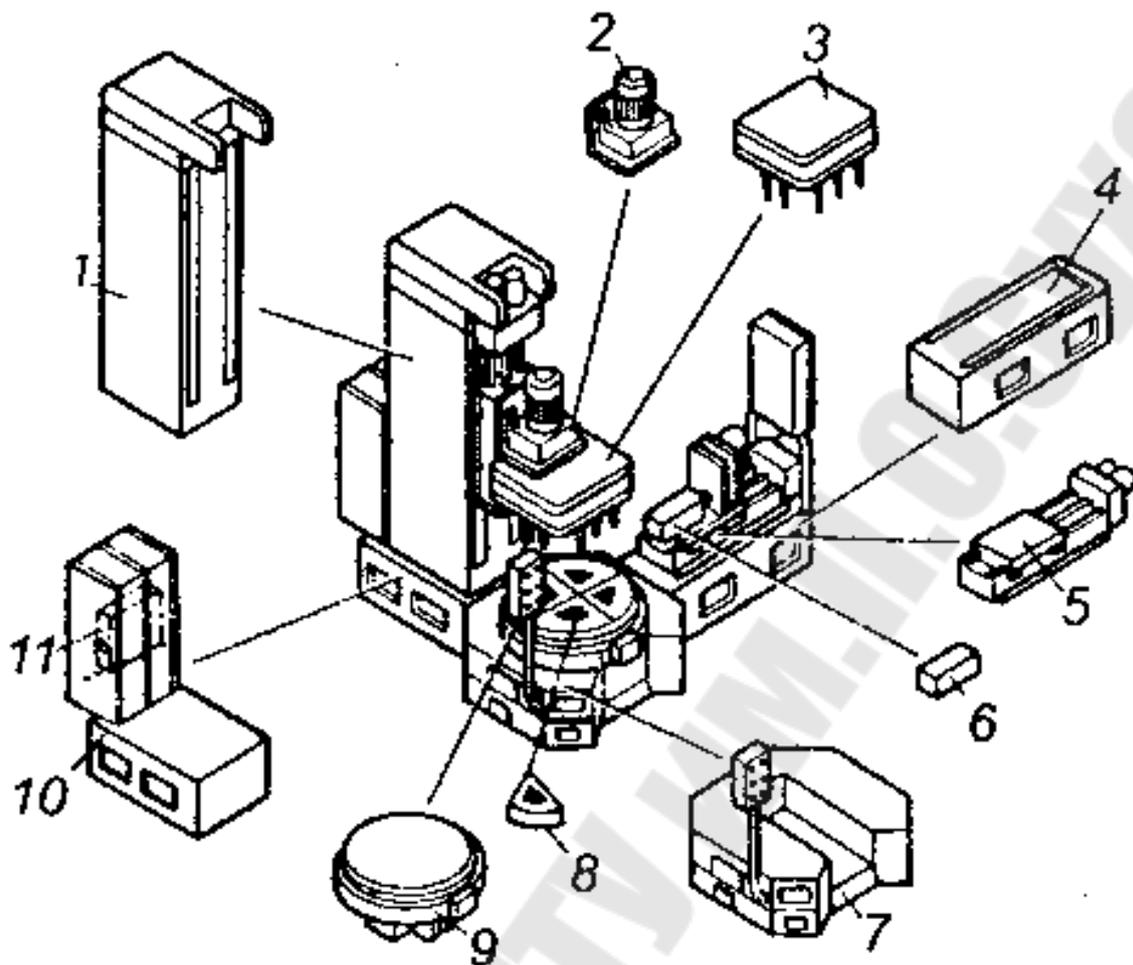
Агрегатный станок из унифицированных агрегатов
